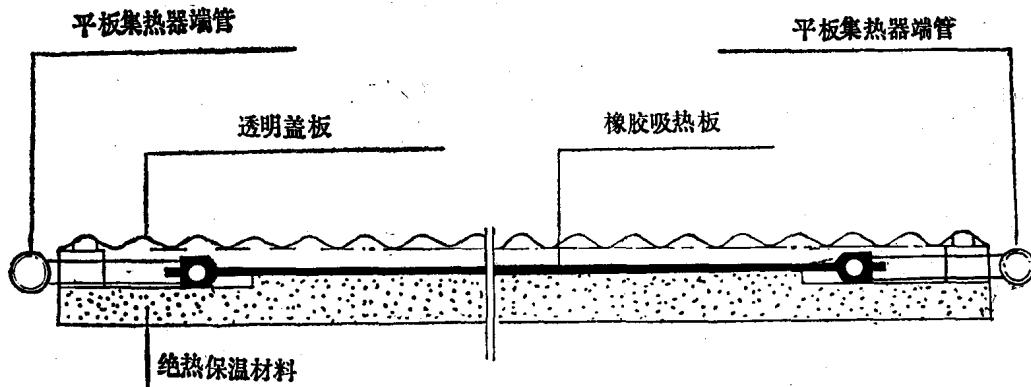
橡胶吸热部件的太阳能平板集热器剖面图
